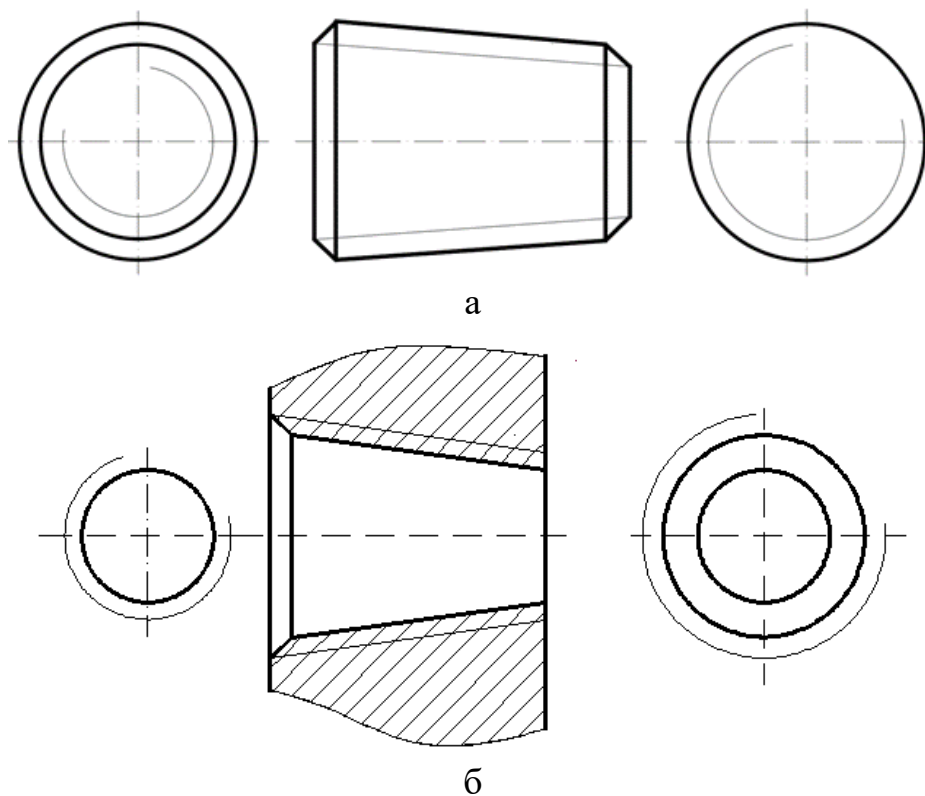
Образец условного изображения конической резьбы: а - наружной, б - в отверстии
